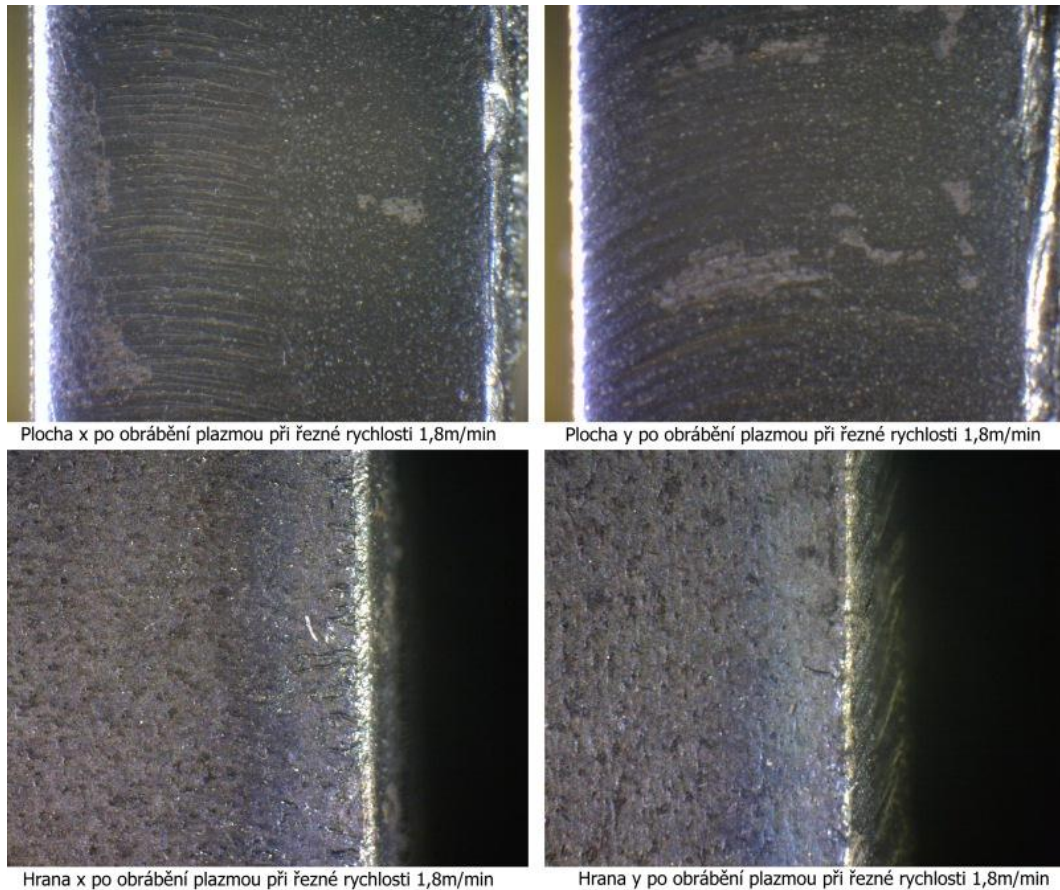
Snímky z mikroskopu vzorku 5 obráběného plazmou - materiál 11 375
